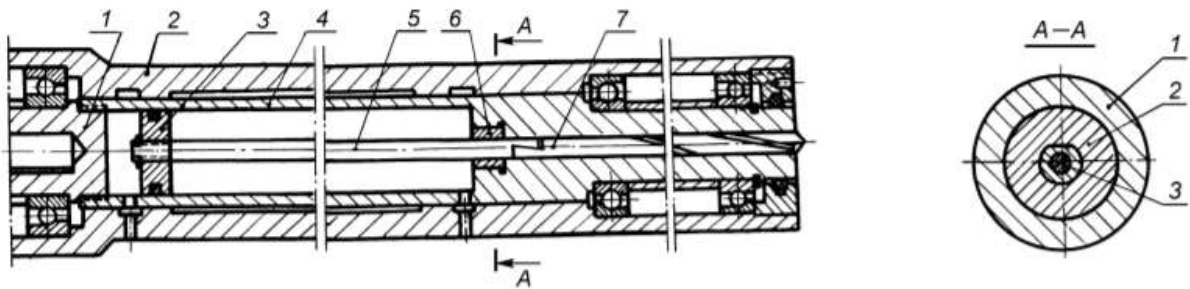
Конструкція механізму привода верстатів для глибокого свердління
